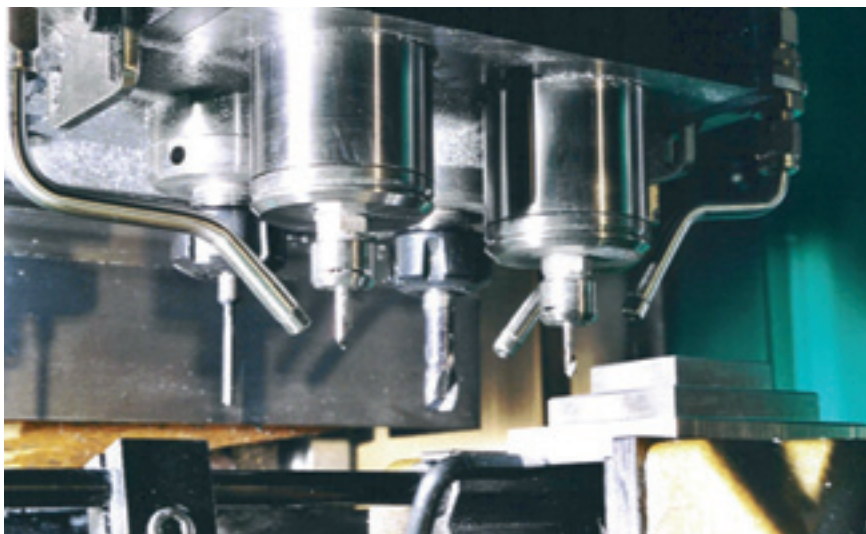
Integriert: F+E-Fräszentrum mit Micro-Innenschmierung (zwei Werkzeugspindeln hinten) und drei lateralen Düsen (zwei HSC-Motorspindeln vorne) für eine optimierte Quasi-Trockenbearbeitung (Bild: Witech SA, Bassecourt)
